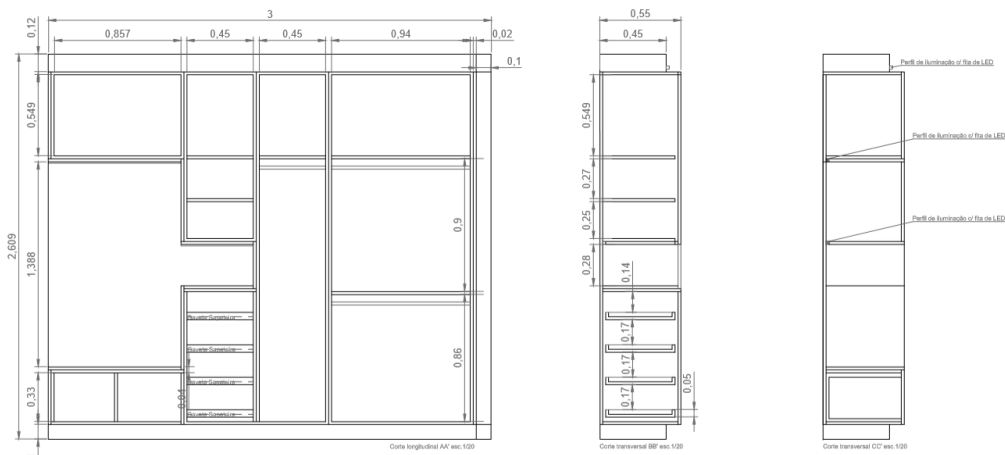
Desenho Técnico Armário. Vistas Principais e Cortes. Escala 1/20. Fonte: autor
